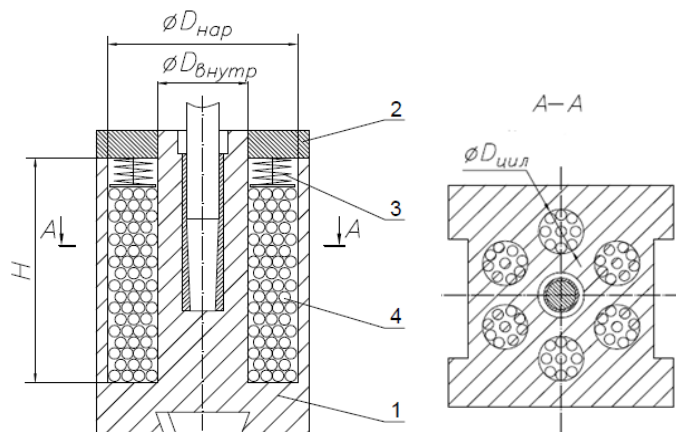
Схема бабы ковочного молота с наполнителем с внутренней полостью в виде N отверстий: 1 – корпус бабы; 2 – крышка бабы; 3 – пружины; 4 –наполнитель (шарики)
